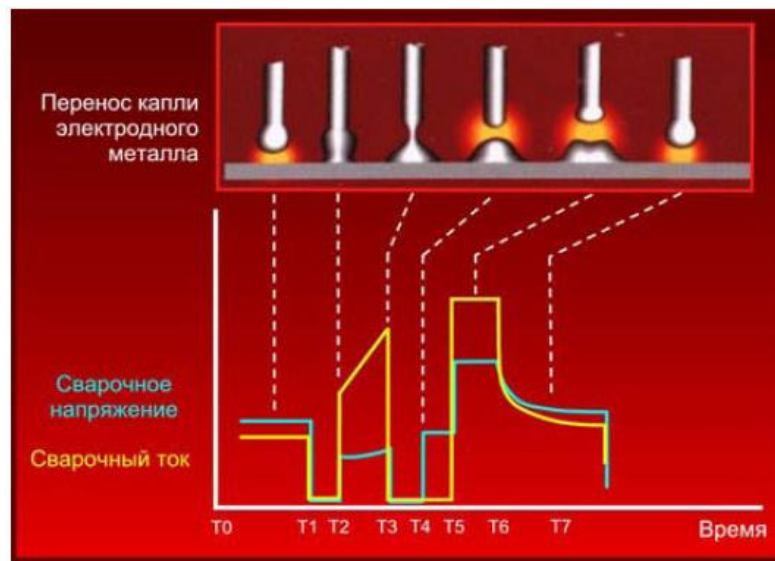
Формы кривых сварочного тока и напряжения при полуавтоматической сварке методом STT [10]
